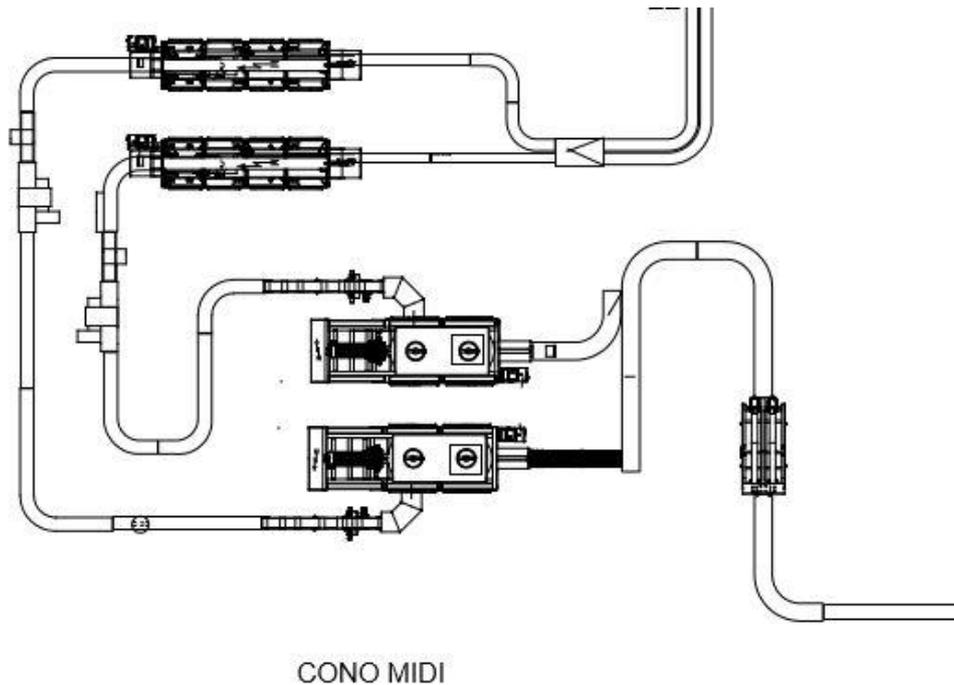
Vista en planta de la zona seca de la línea CONO-MIDI
